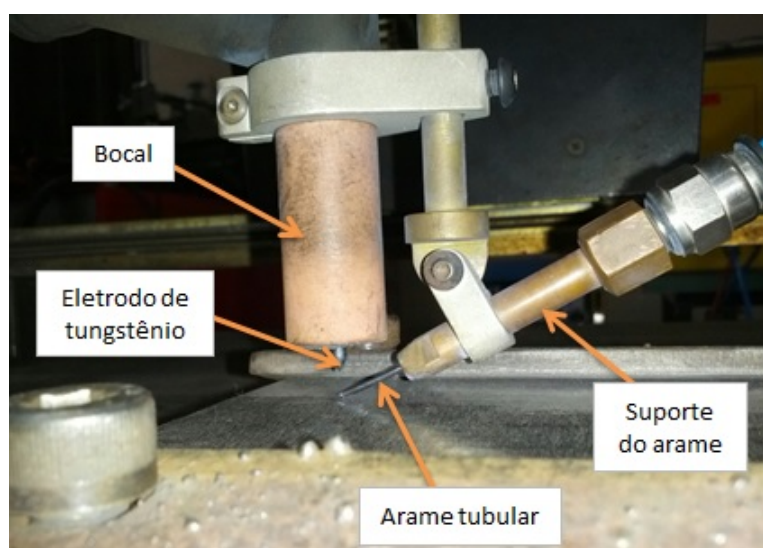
Tocha de soldagem TIG que será utilizada para depositar os cordões e revestimentos. Fonte: autoria própria. Fonte: Autoria própria
